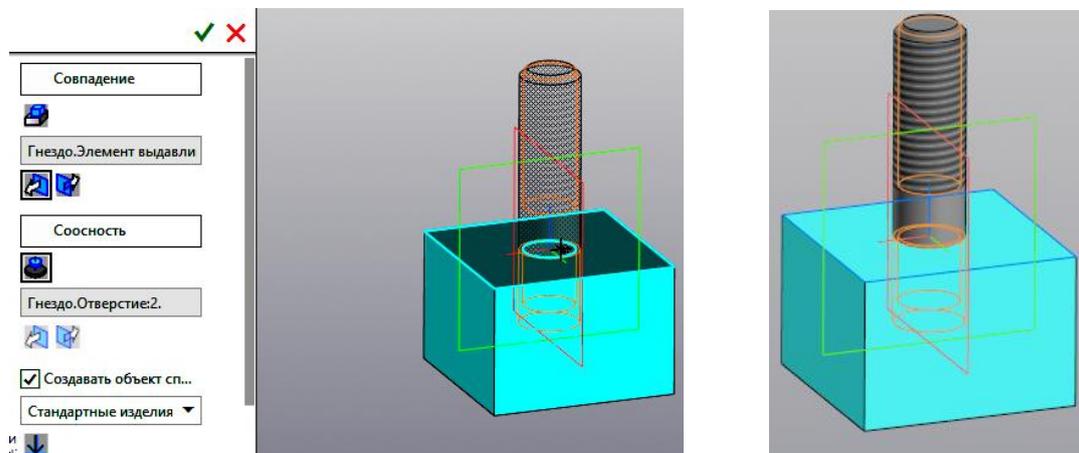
Размещение шпильки в гнезде корпусной пластины
